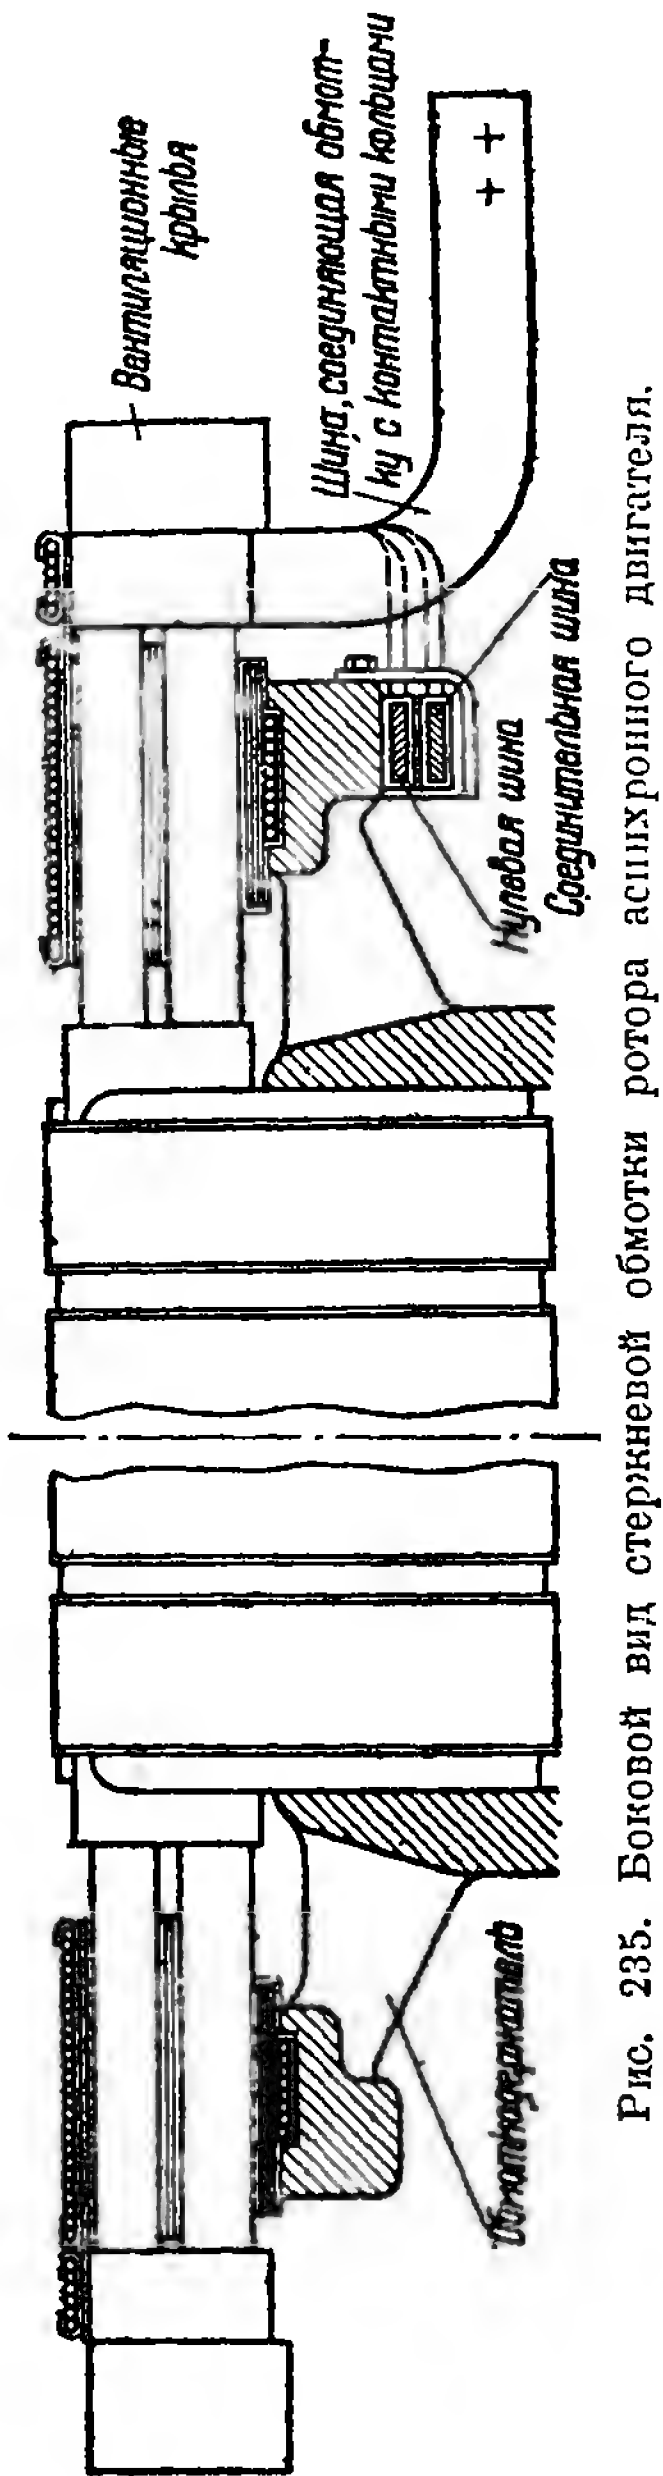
Боковой вид стержневой обмотки ротора асинхронного двигателя.
